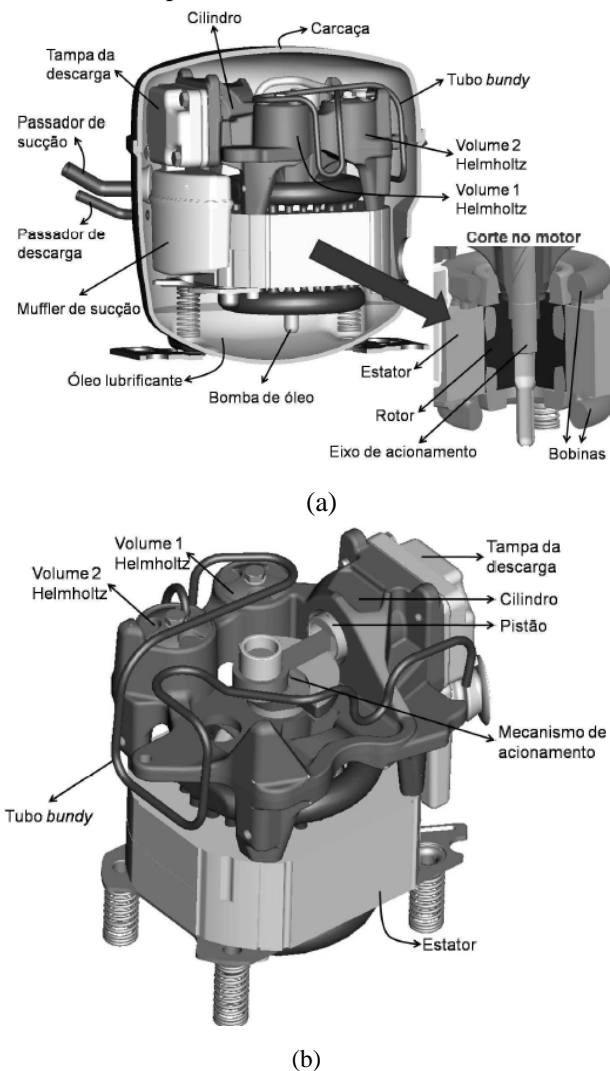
Compressor EGX90HLC: (a) Vista lateral em corte e detalhe do motor; (b) vista isométrica.
